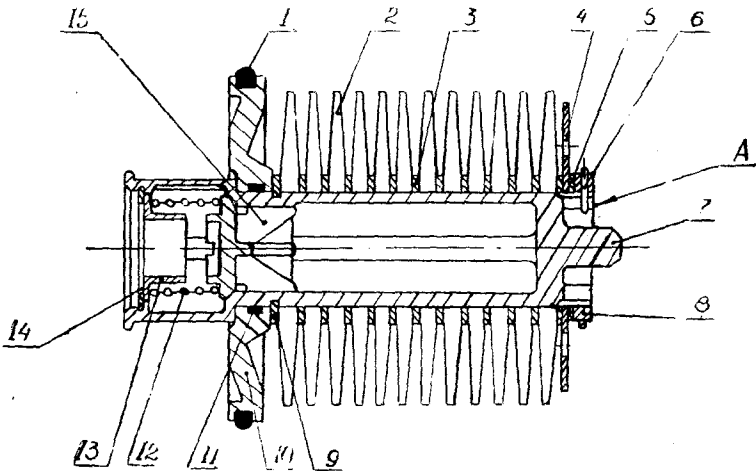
а. Масляный фильтр двигателя ТВ2-117АГ со стяжной гайкой пакета фильтрующих элементов.
